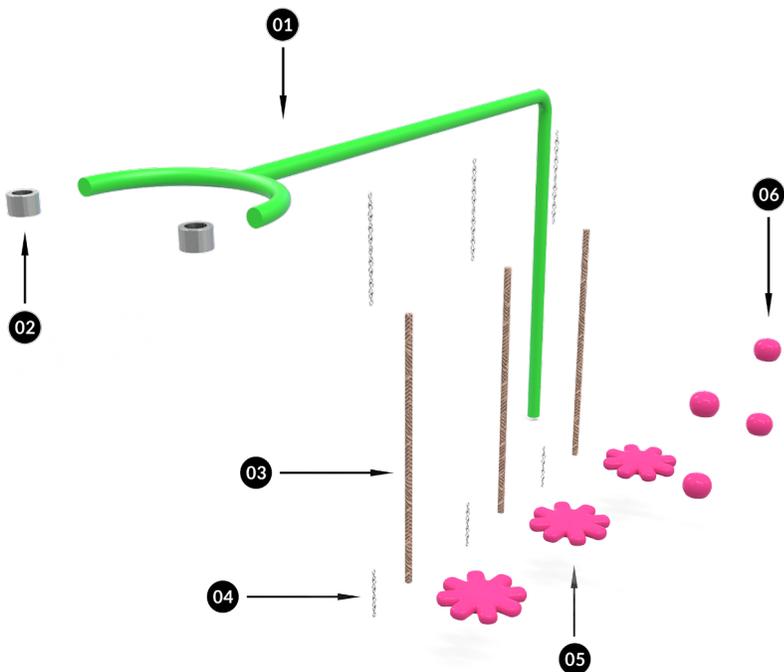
Escalada com corda fixa explodida, fonte: Autora.
